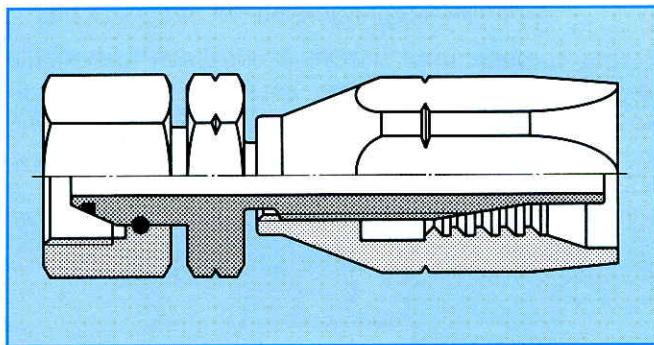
Резьбовое соединение с уплотняющей отбортовкой, промежуточным кольцом и мягкими прокладками. Фиксация обеспечивается за счёт отбортовки под углом 37° на промежуточном кольце.
